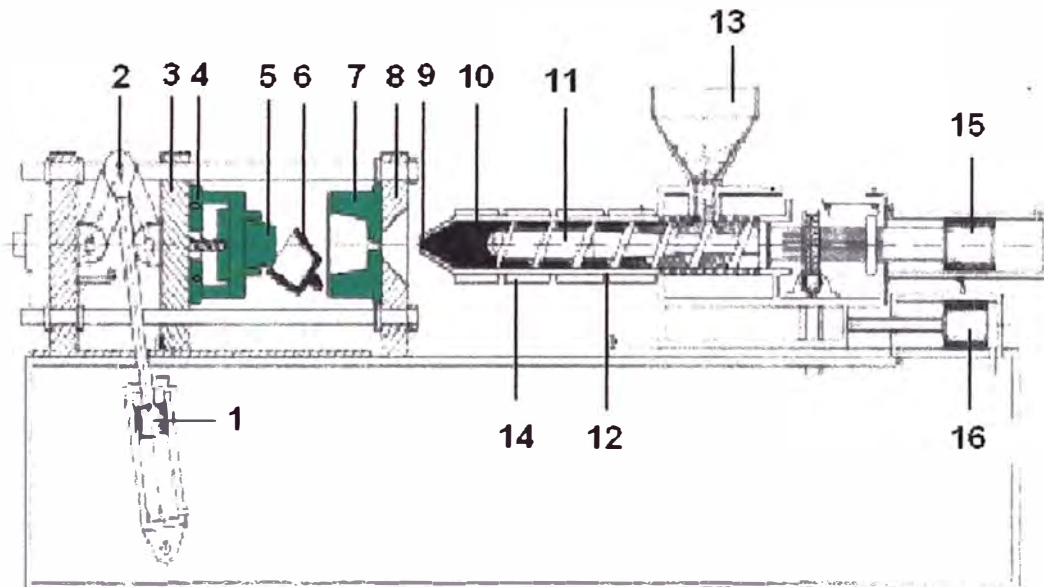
Máquina de Inyección de Husillo Reciprocante
